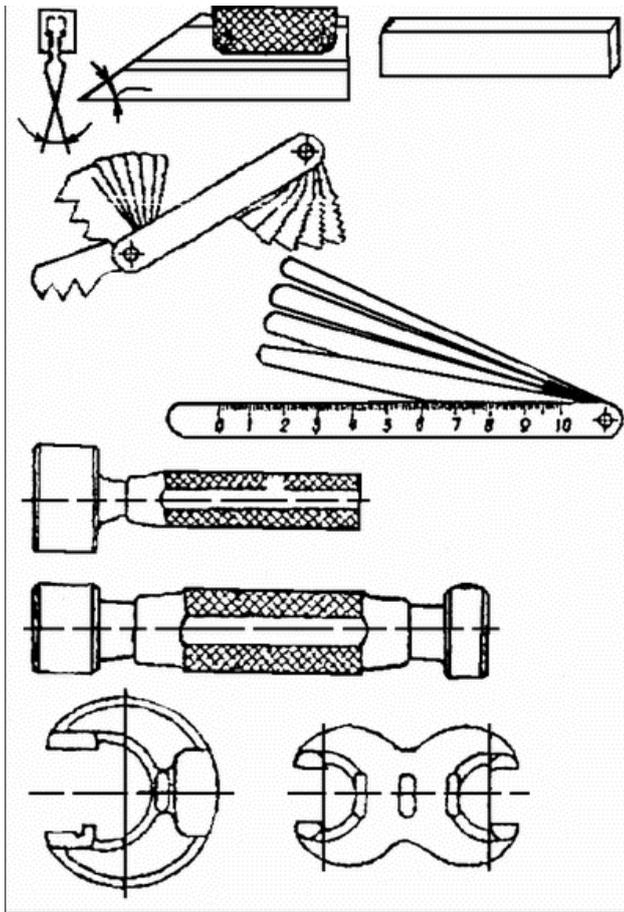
Простые специальные инструменты для контроля размеров: а – линейка угловая с двухсторонним скосом; б – линейка прямоугольная; в – шаблон резьбовой; г – шуп; д – пробка сборная односторонняя; е – пробка сборная двухсторонняя предельная; ж – скоба предельная односторонняя; з – скоба предельная двухсторонняя
